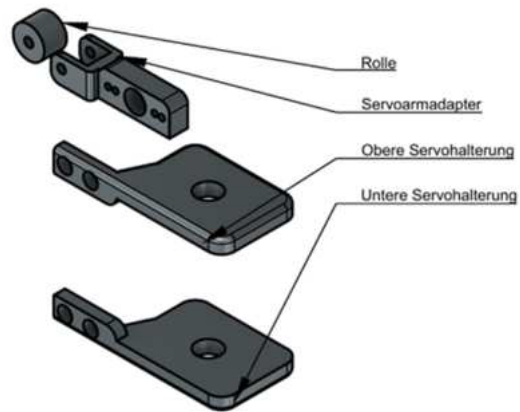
3D-gedruckte Komponenten des Auslösemechanismus
